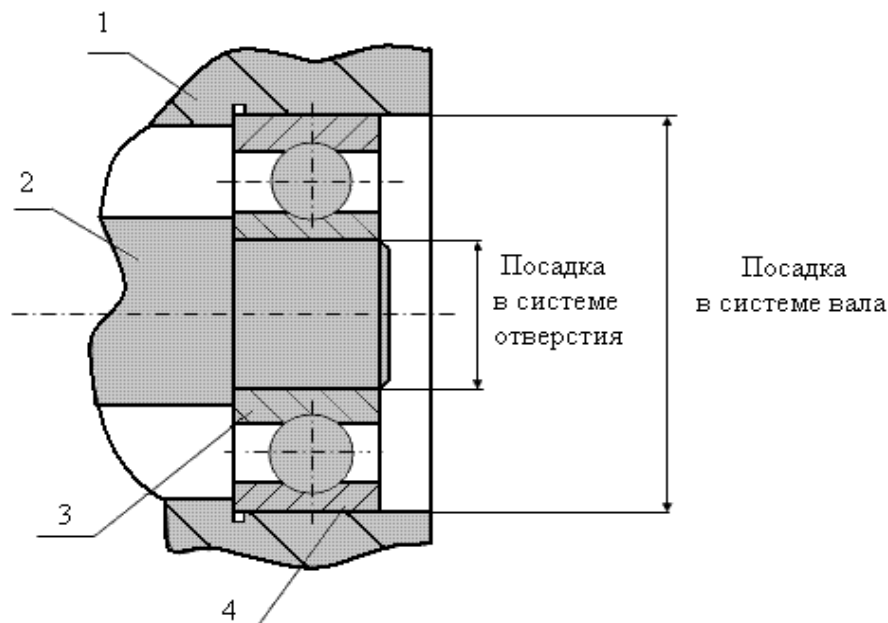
Пример посадки в системе вала и системе отверстия, 1 – корпус; 2 – вал; 3 – внутреннее кольцо подшипника, 4 – наружное кольцо подшипника
